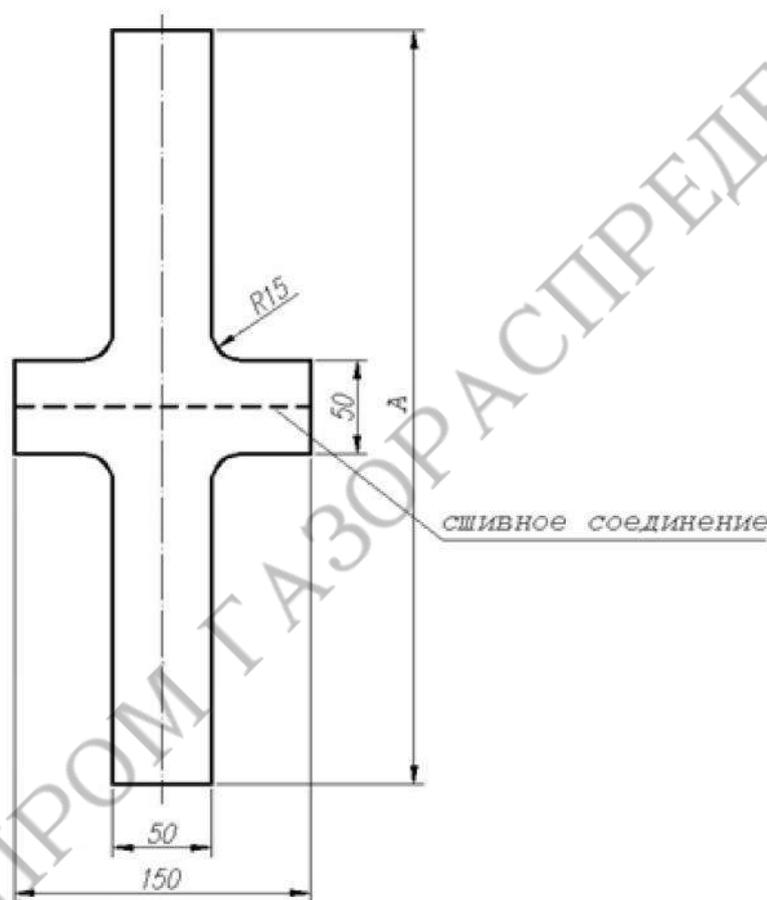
Схема образца для испытания сшивного соединения (сшивное соединение показано условно) не по центру
